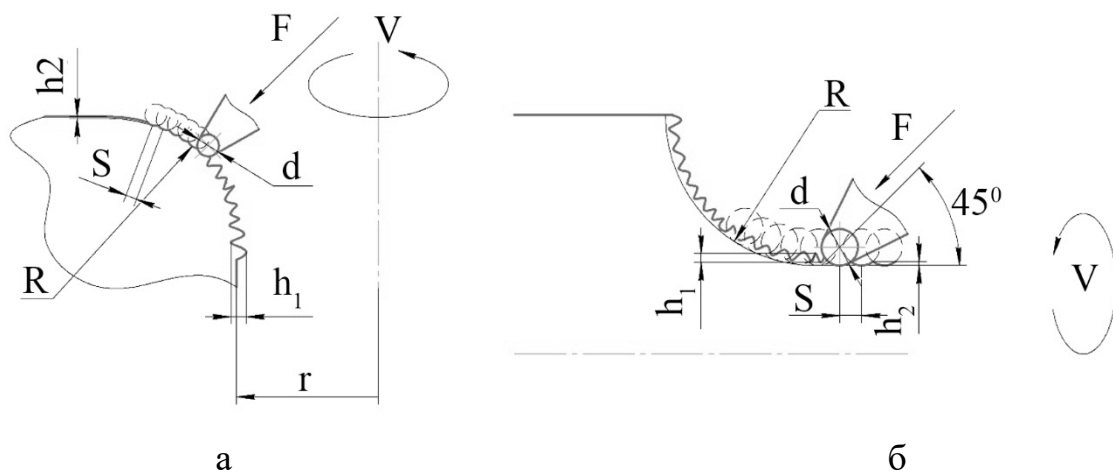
Кінематична схема зміцнення конструктивних концентраторів напружень алмазним вигладжуванням: а – обробка поверхні переходу отвору у площину; б – обробка поверхні типу «Поверхня поєднання двох діаметрів»
